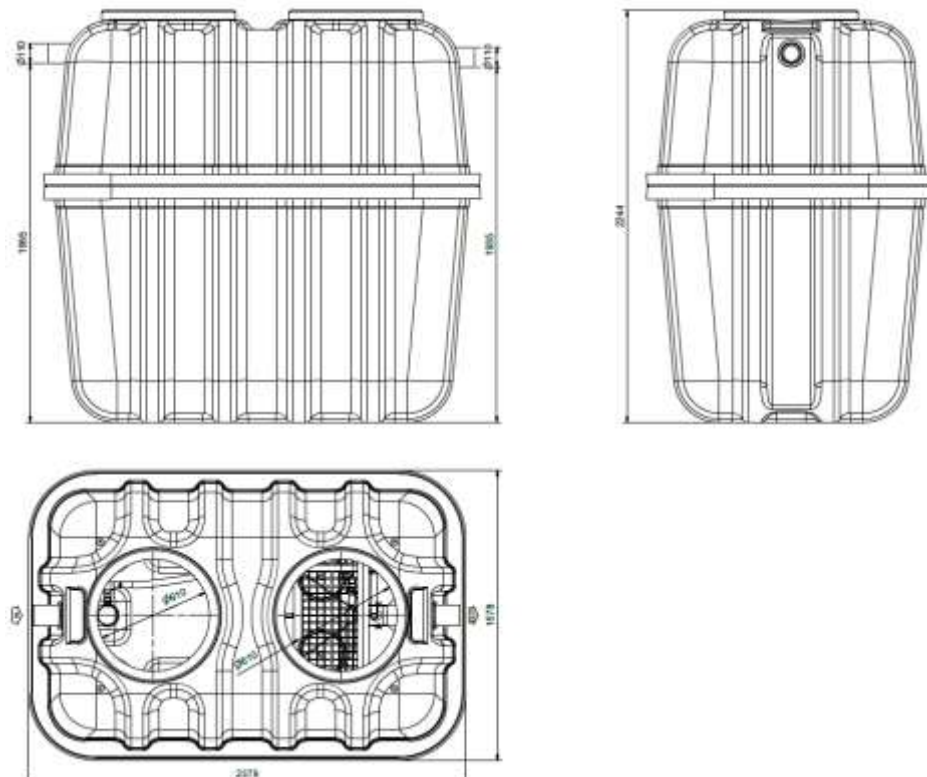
Plan d'encombrement d'une cuve de 6000L
